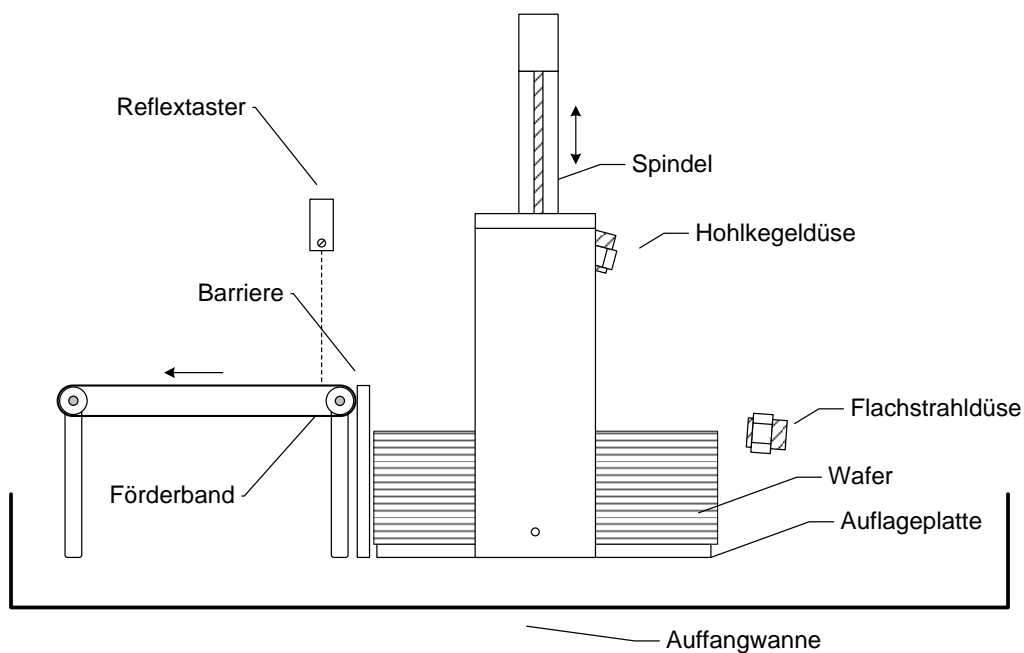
Prinzipzeichnung mit den wichtigsten Komponenten des Prototypen
